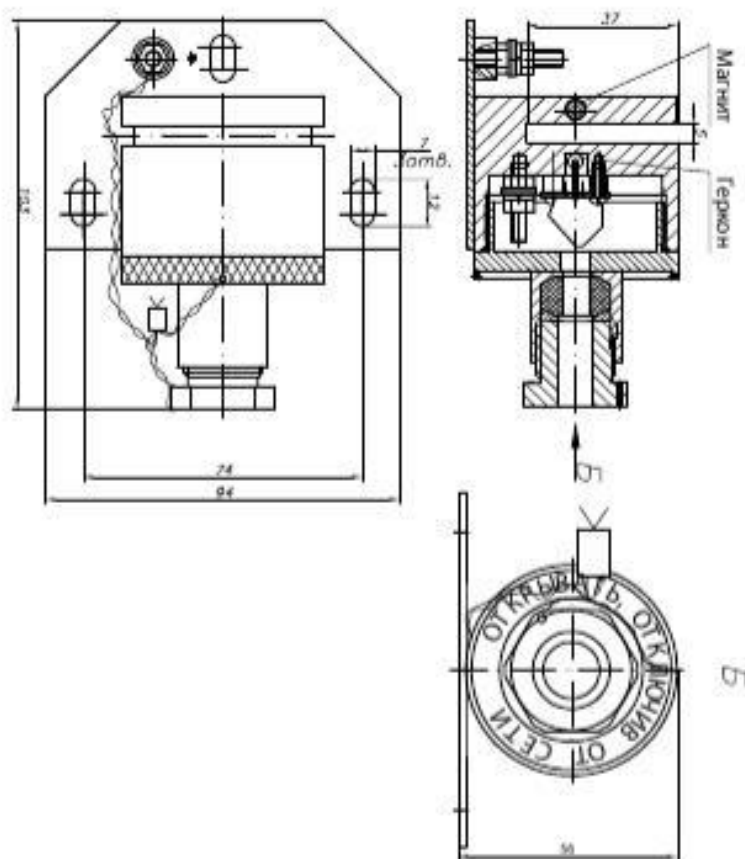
Габаритные и присоединительные размеры МГДУ КП модели 04.
